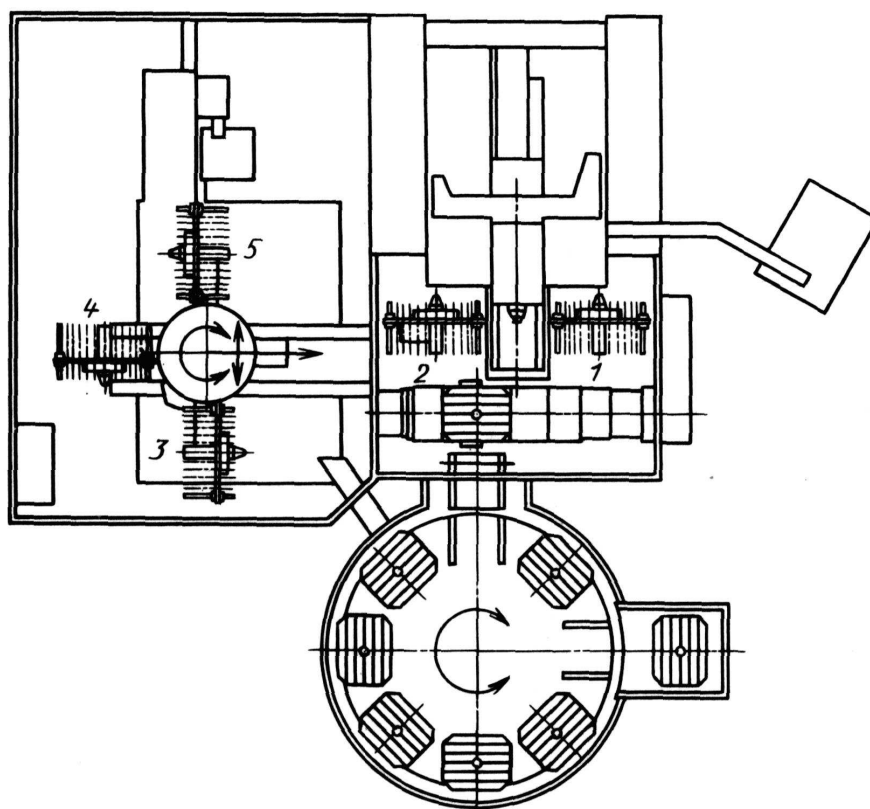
Многоцелевой станок с дисковыми инструментальными магазинами фирмы «Хюллер Хилле»
